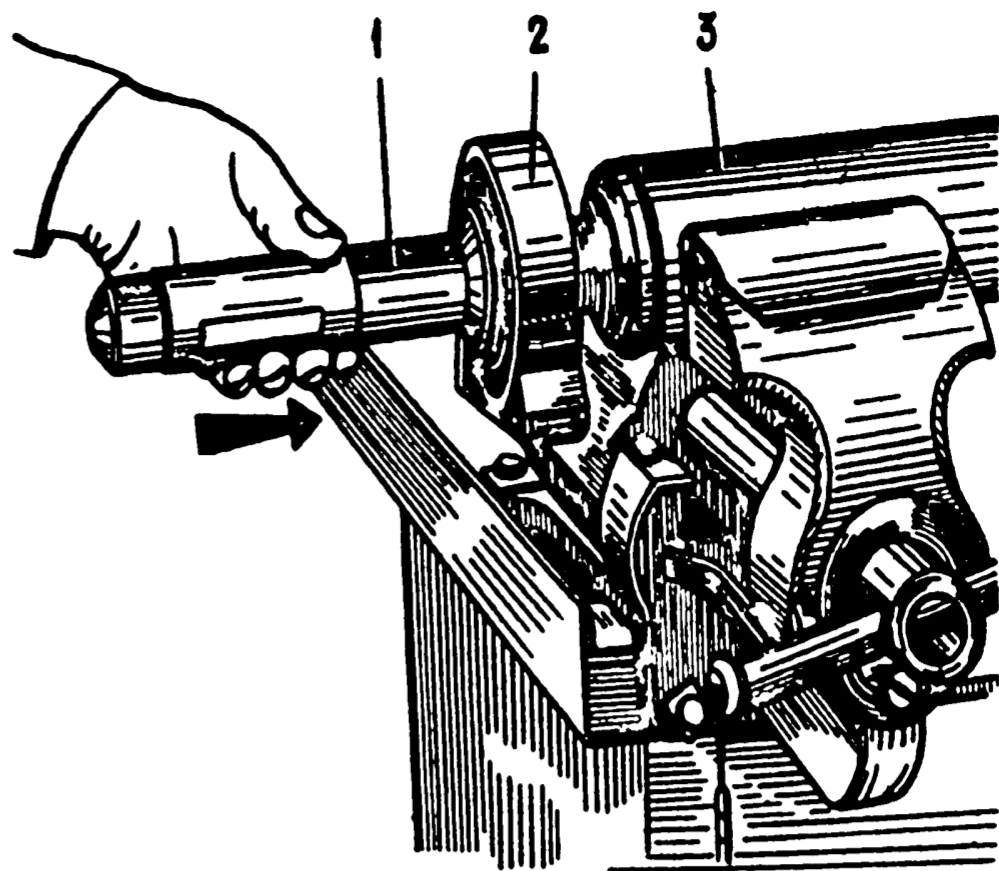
Установка упругой опоры на передний карданный вал: 1 - оправка А.74035; 2 - упругая опора; 3 - задняя часть переднего карданного вала
